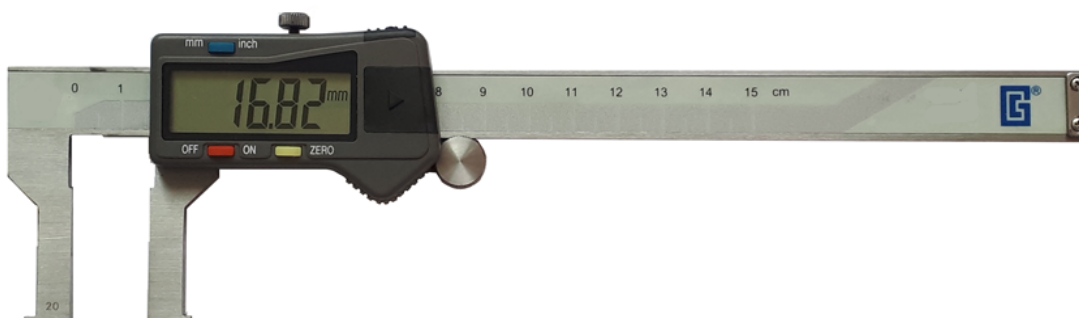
Общий вид штангенциркулей модели ШЦЦС-115
